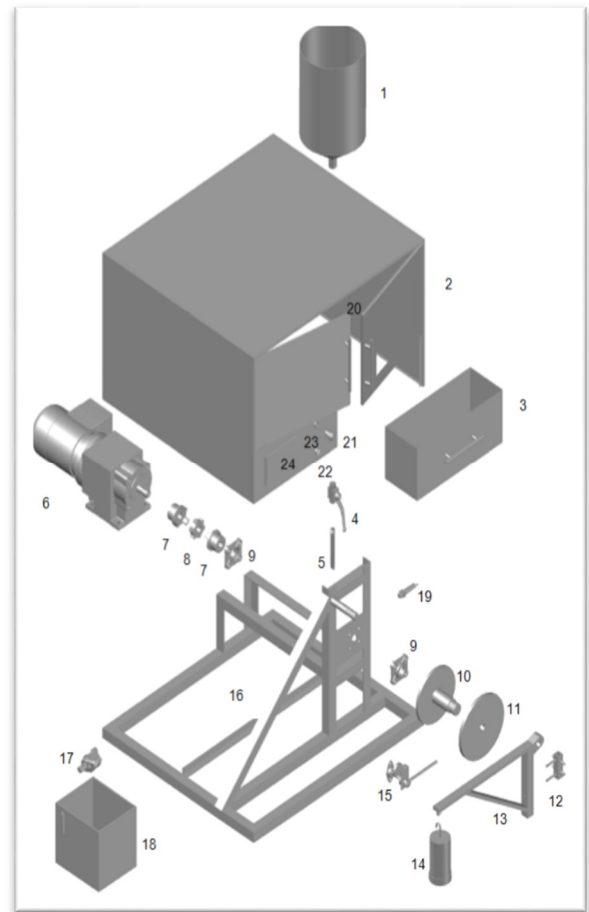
Despiece del equipo de desgaste abrasivo norma astm g-65.
